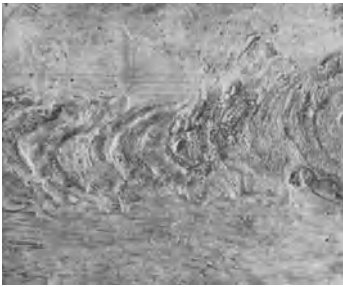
Mit dem Kohlelichtbogen geschweißtes Kupferblech.
